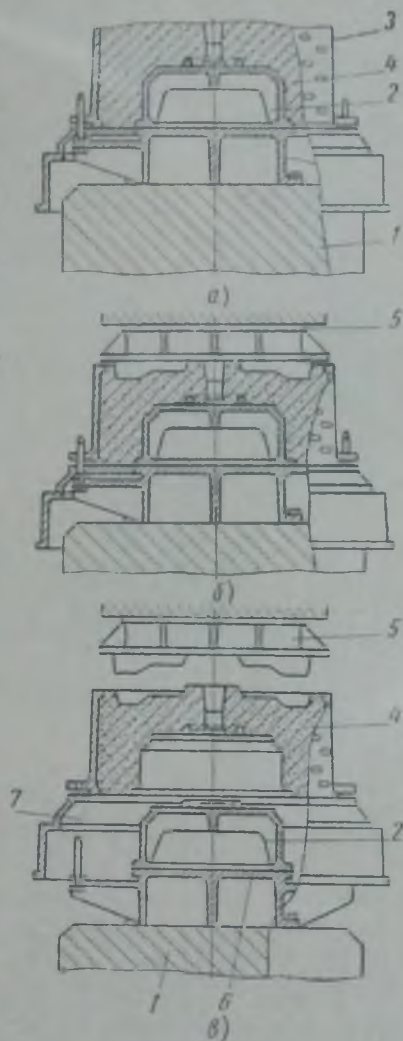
Схема изготовления верхней полуформы для отливки тормозного барабана
